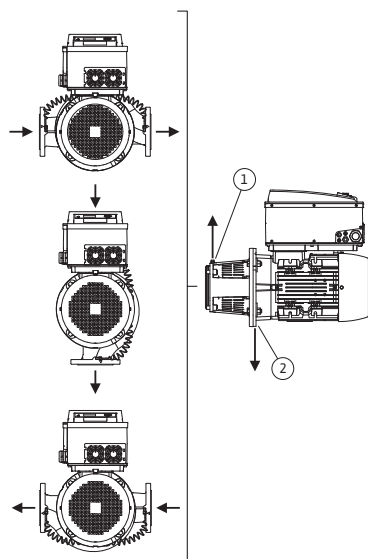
Přípustné polohy instalace s vodorovnou hřídelí motoru
